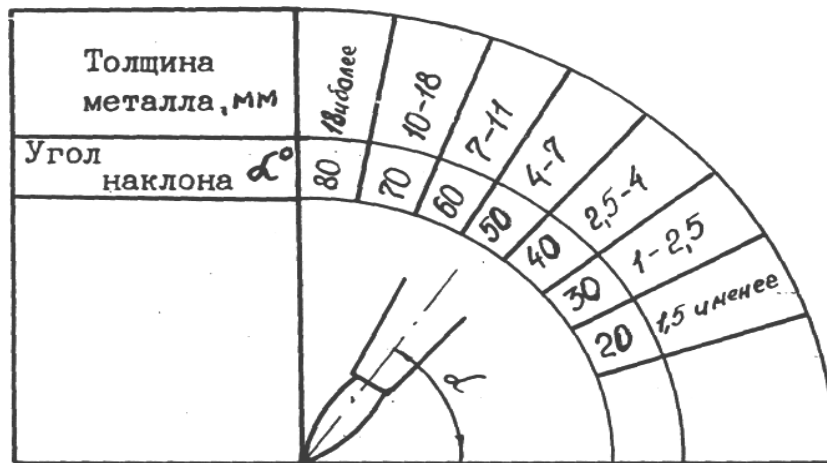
Рекомендуемые углы наклона газовой горелки при сварке металла различной толщины
